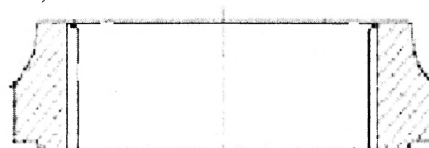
Фрагмент внутренней цилиндрической части детали ступица шестерни
